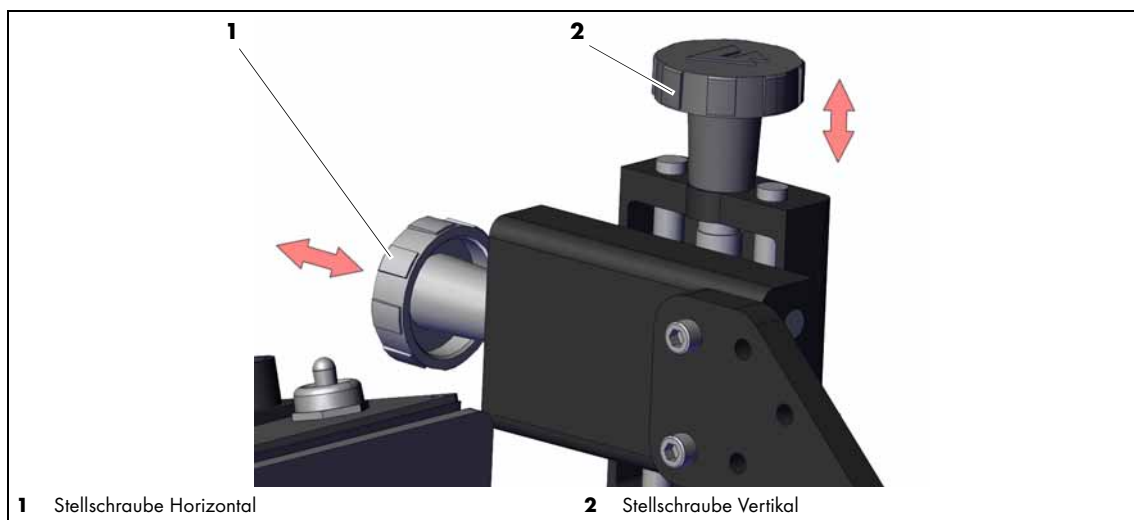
Feinjustierung des Kreuzsupports bei der Schweißbrennermontage
